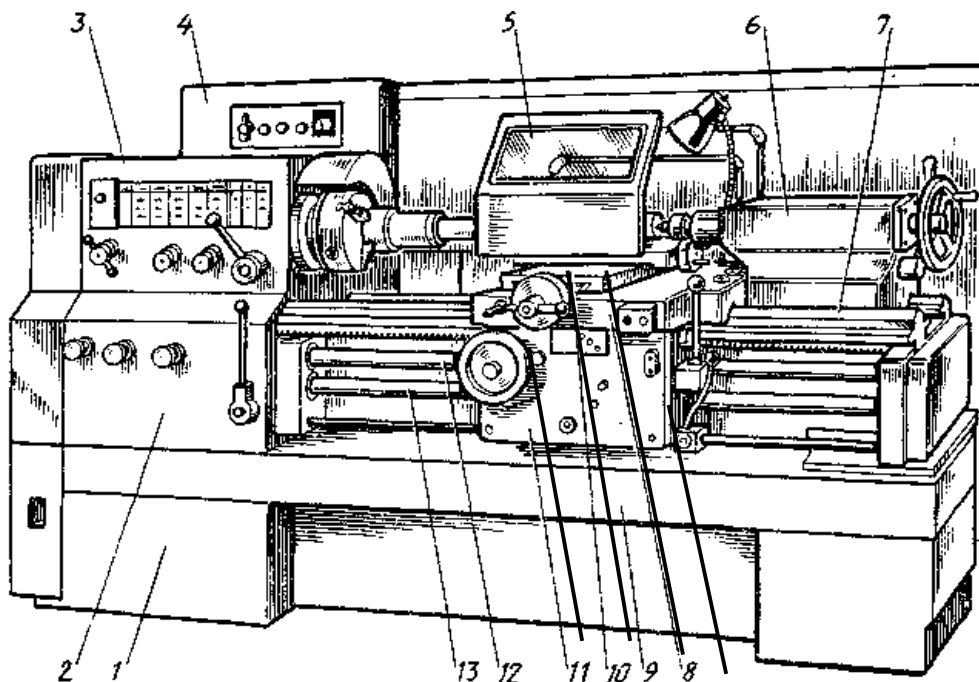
Внешний вид токарно-винторезного станка модели 16К20
